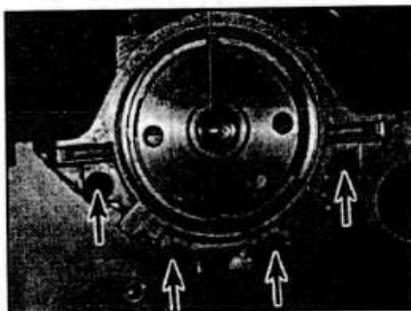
С.60. Расположение болтов крепления крышки уплотнительного кольца.
